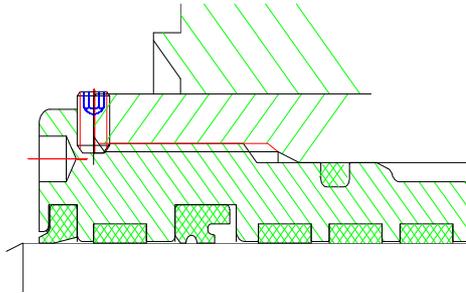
Führungsmutter mit Nutring, O-Ring und Führungsringen
